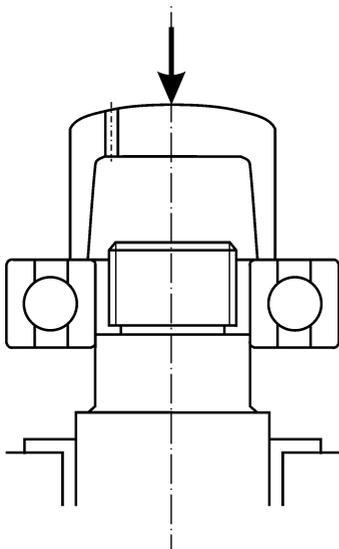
Установка с натягом внутреннего кольца подшипника
